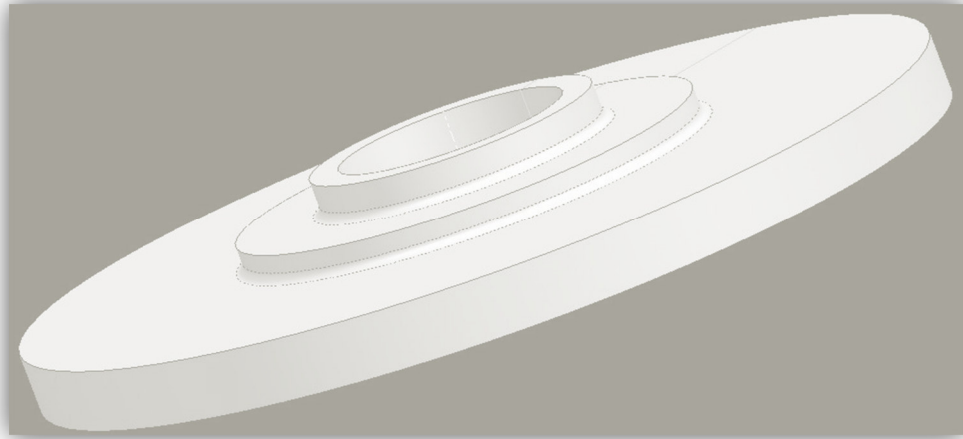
Заготовка диска 5 ст. КВД из титанового сплава с центральным отверстием диаметром 120 мм
